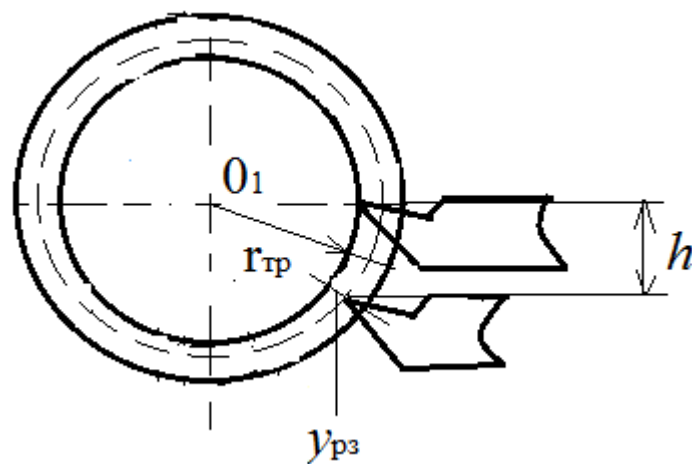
Вплив на розмір деталі зміщення вершини різця
